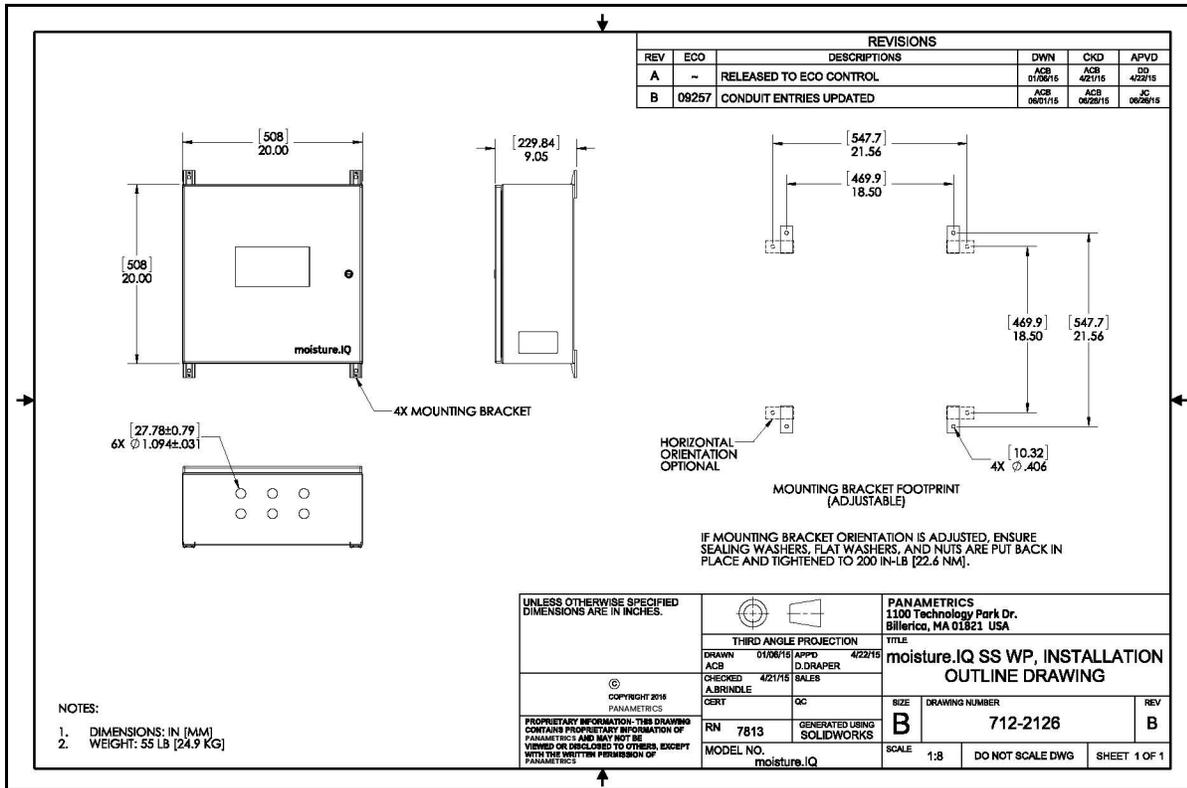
Plano esquemático de instalación SS WP (Plano 712-2126_revB, SH 1 de 1)
